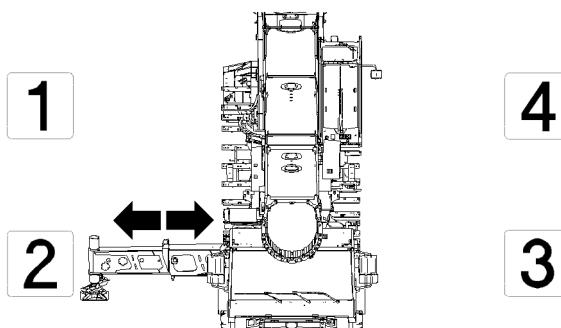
Posicionamiento de la viga corredera de apoyo
